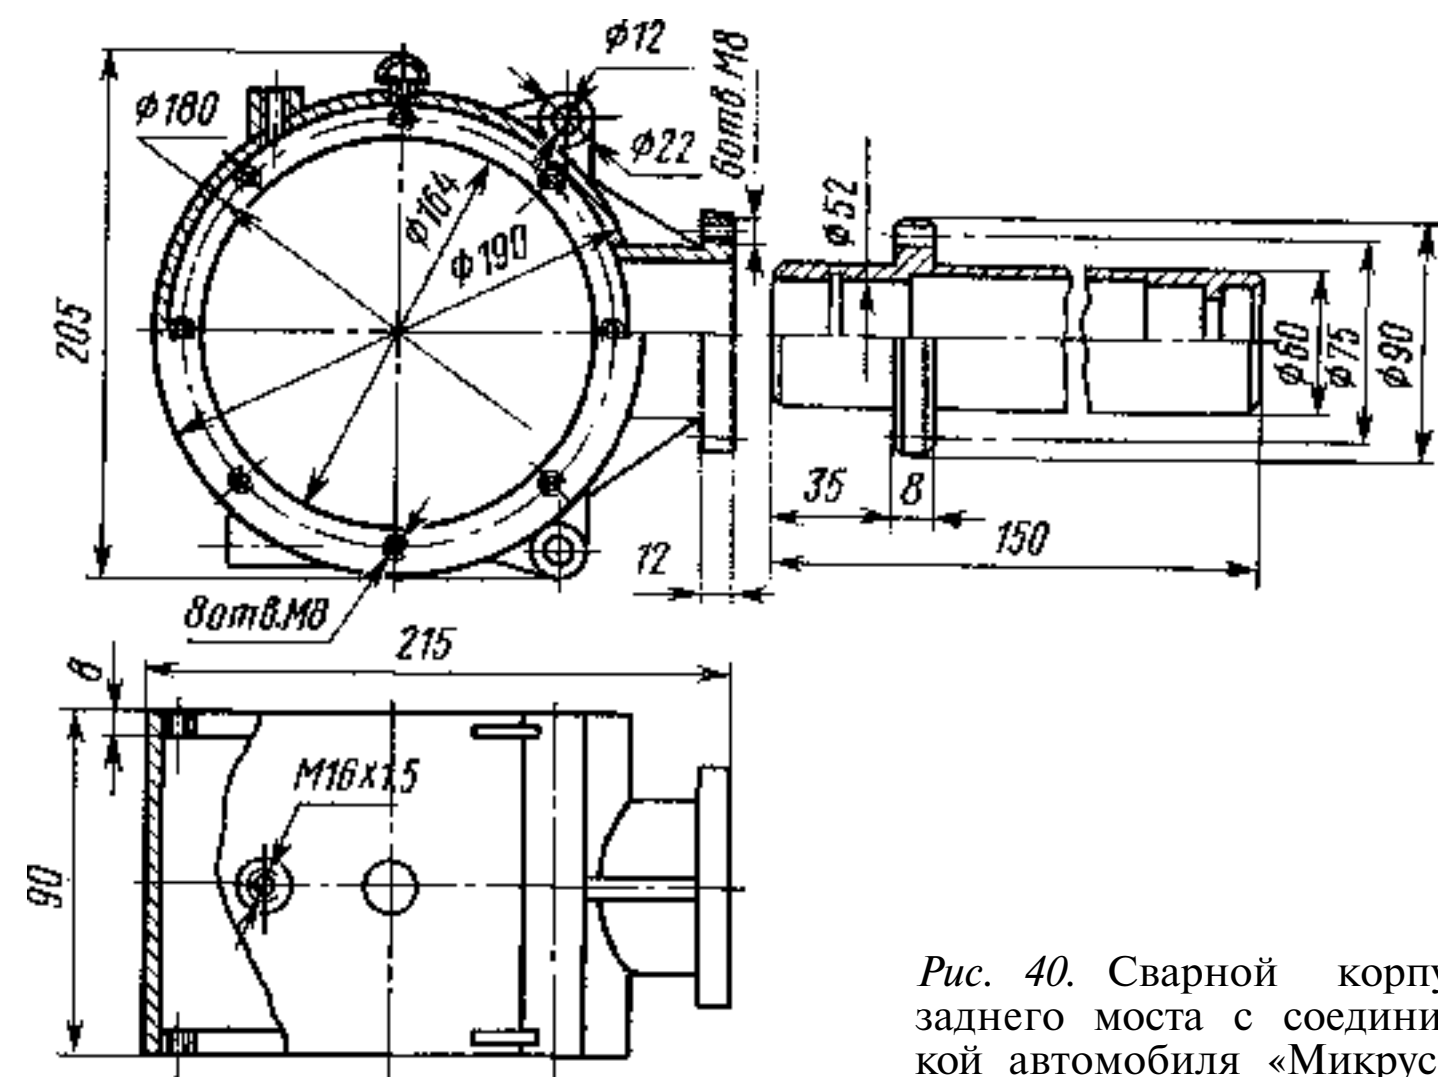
Сварной корпус редуктора заднего моста с соединительной втулкой автомобиля «Микрус»
